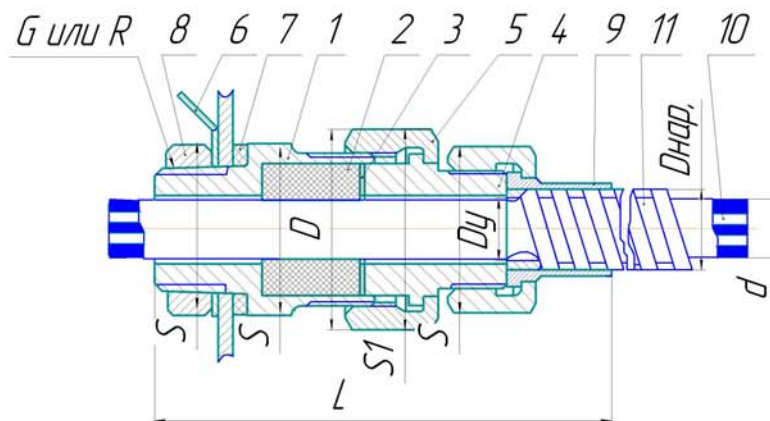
Состав и присоединительные размеры коробки соединительной
